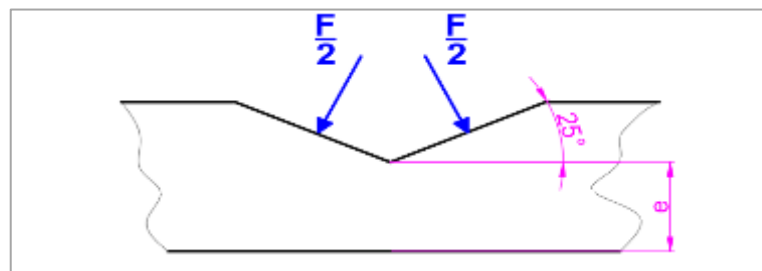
Diagrama de fuerzas de tracción en la garganta
